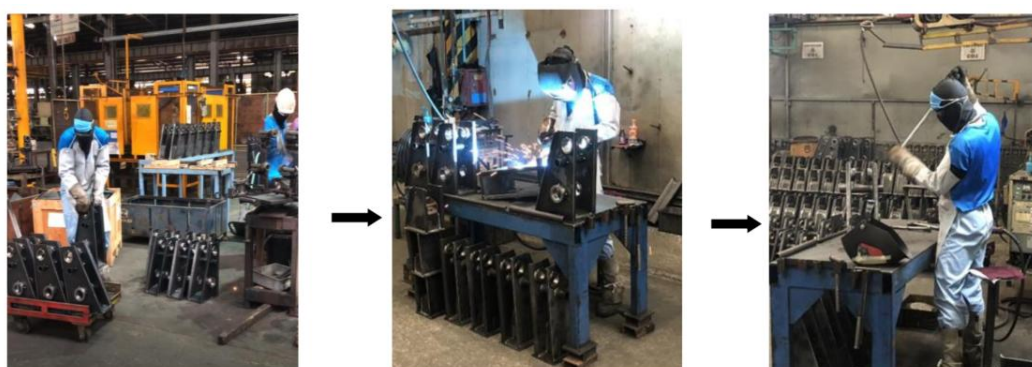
ขั้นตอน Tack Weld
